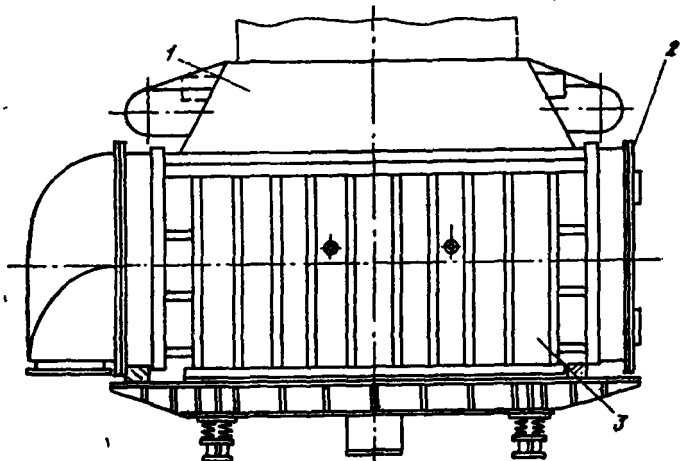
Корпус конденсатора турбины К-300-240:
